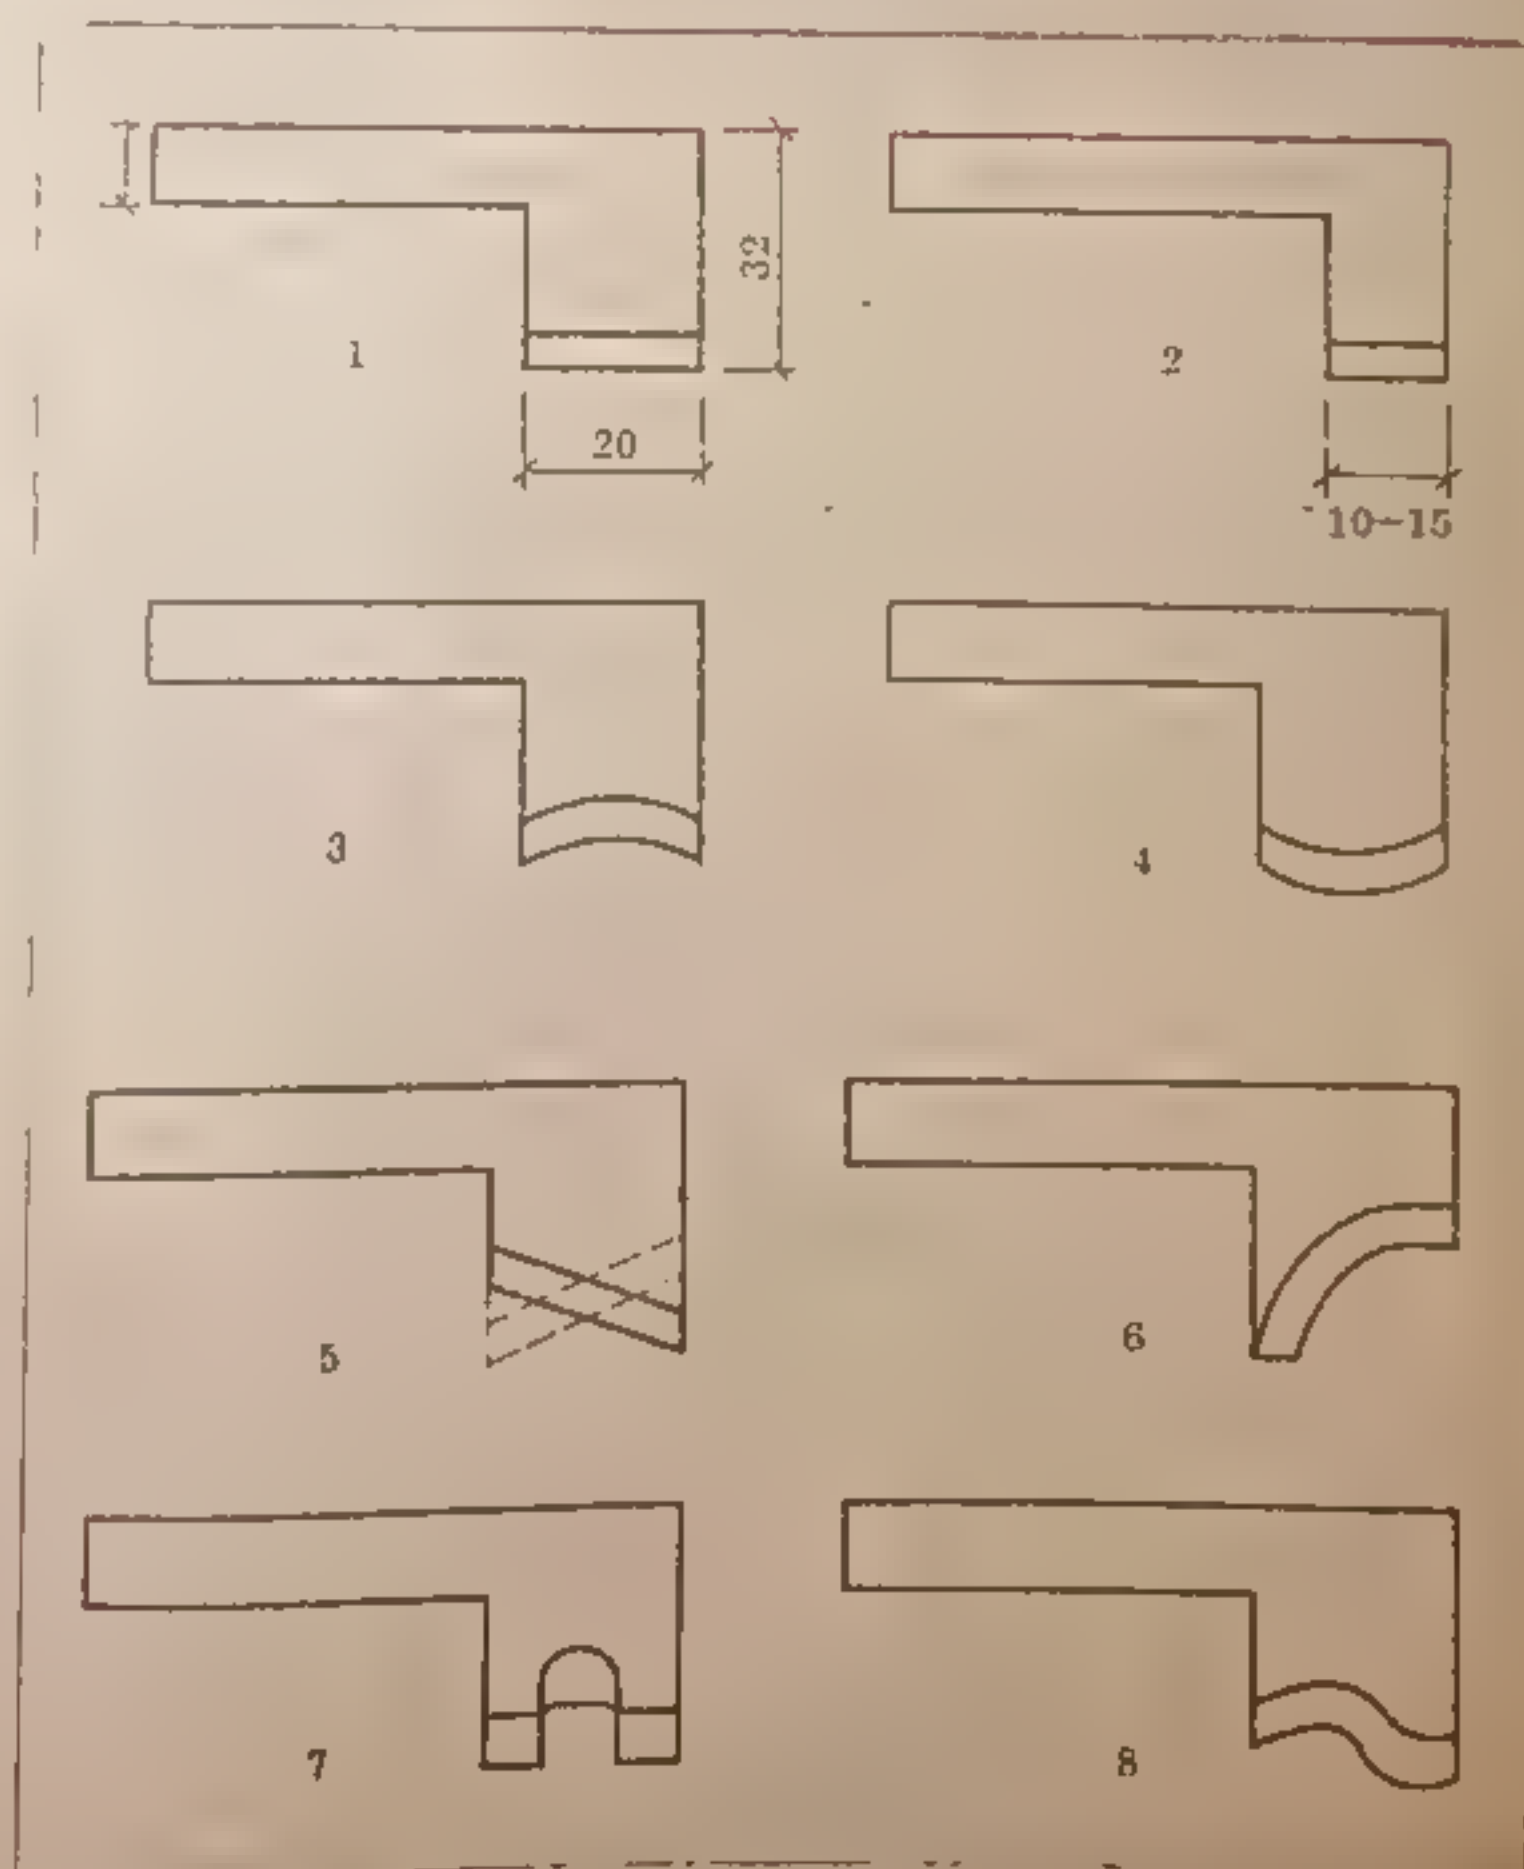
Самодельные ножи: 1, 2 — для выборки пазов и четвертей; 3 — создания овала; 4 — выборки желоба; 5 — снятия фаски; 6 — изготовления штапиков; 7 — выборки шипов; 8 — изготовления наличников
